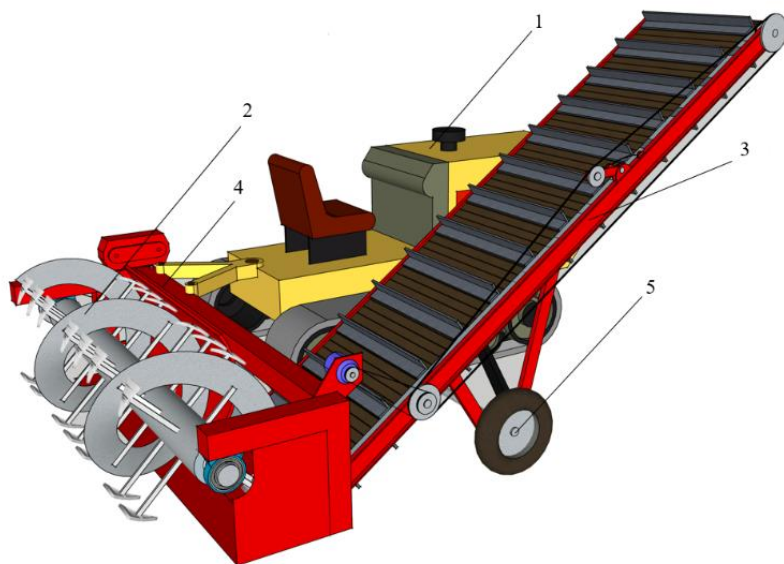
Схема погрузчика-смесителя: 1 – гусеничный трактор; 2 – рабочий орган; 3 – отгрузочный транспортер; 4 – рама; 5 – колесо
